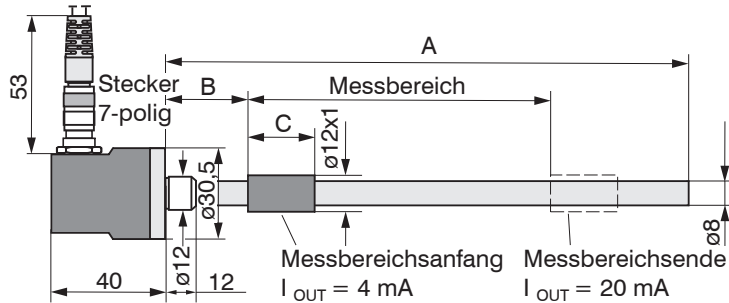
Maßzeichnung Gehäuseausführung ZA
